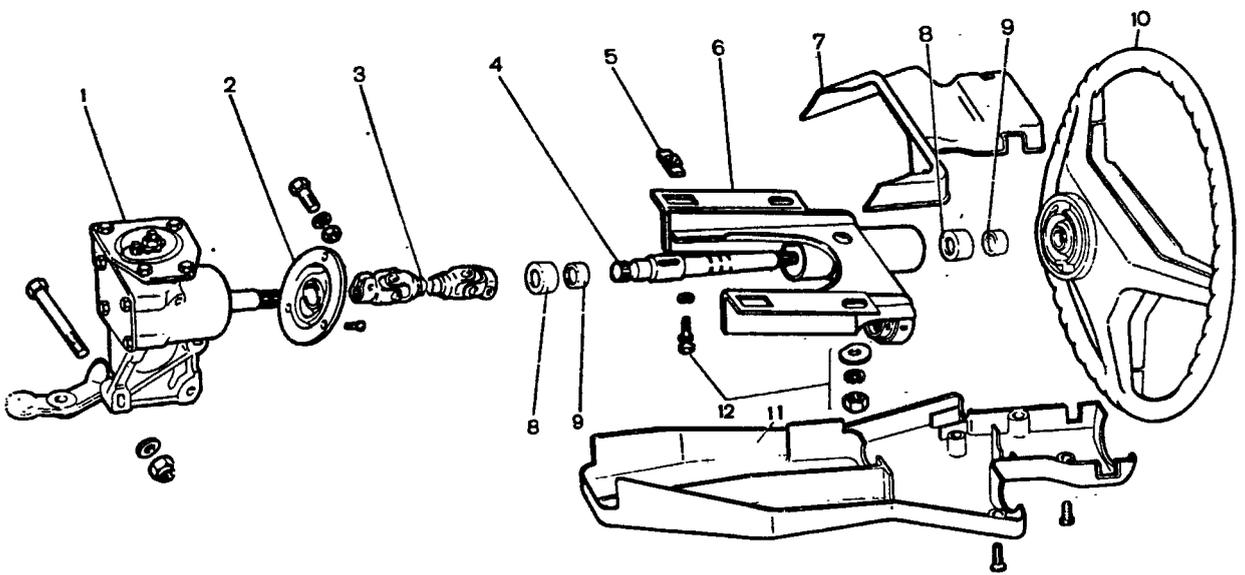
Детали рулевого механизма: 1 - картер рулевого механизма; 2 - уплотнитель вала; 3 - промежуточный вал; 4 - верхний вал; 5 - фиксирующая пластина передней части кронштейна; 6 - кронштейн крепления вала рулевого управления; 7 - верхняя часть облицовочного кожуха; 8 - вилка подшипника; 9 - подшипник; 10 - рулевое колесо; 11 - нижняя часть облицовочного кожуха; 12 - детали крепления кронштейна
